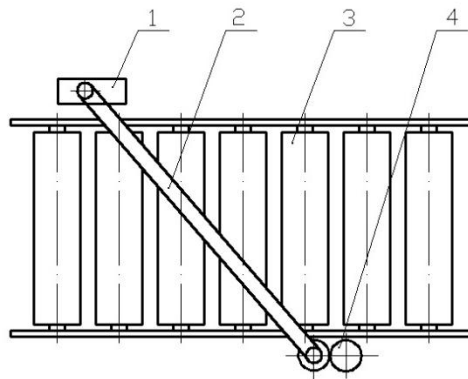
Плуговий скидач з приводною стрічкою: 1 – фіксатор; 2 – плуг; 3 – пластинчатий конвеєр; 4 – привод
